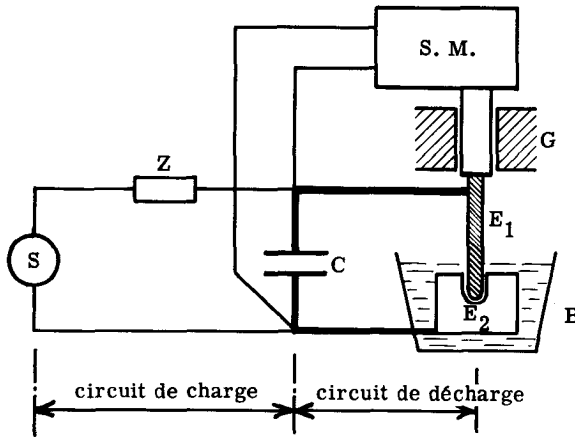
Schéma de principe d'une machine à usiner par électro-érosion
